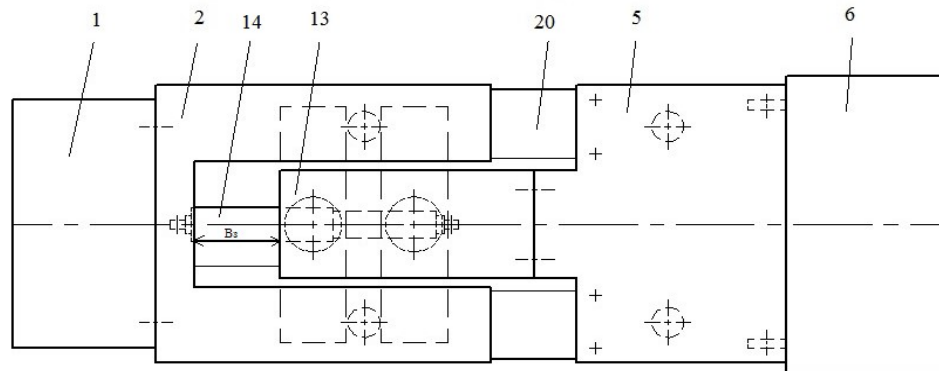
Секция гидрофицированной крепи с выдвинутой забойной ступенью перекрытия (вид сверху)
